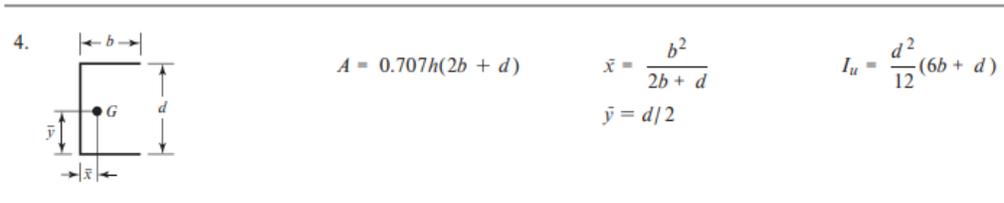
Propiedades flexionantes de las soldaduras de filete. Fuente: Elaboración propia.
